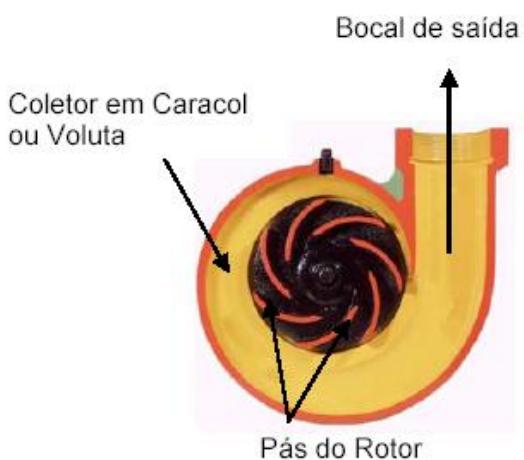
Vista frontal do caracol e rotor em corte de uma bomba centrífuga.
